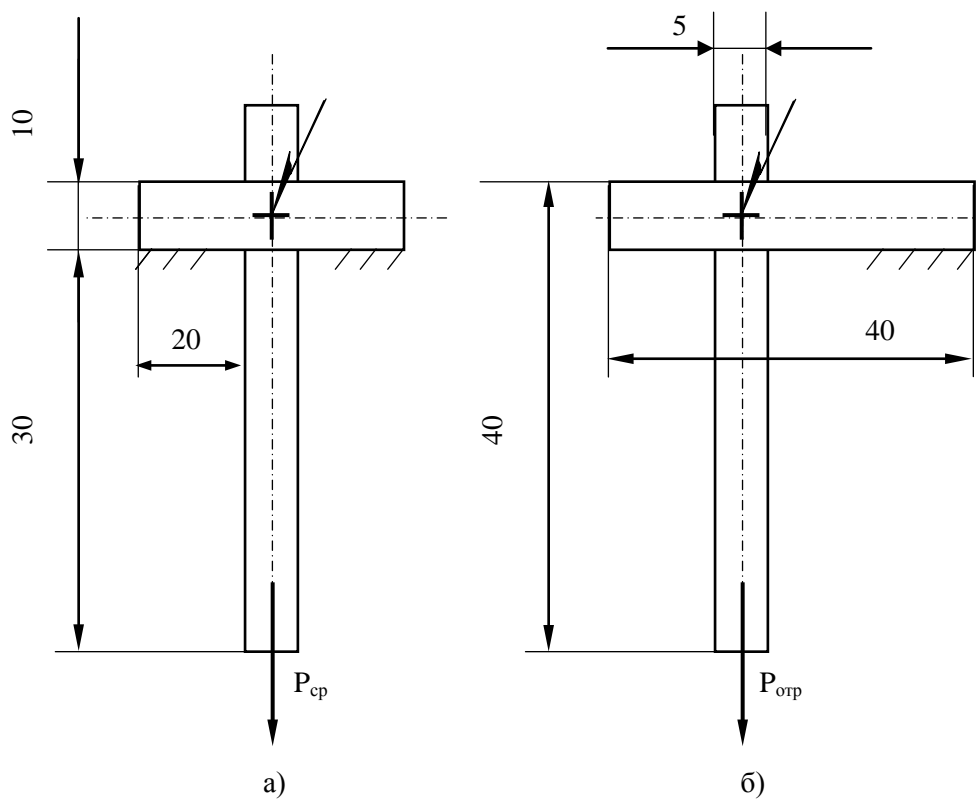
Схемы испытания сварных соединений на срез (а) и на отрыв (б).
